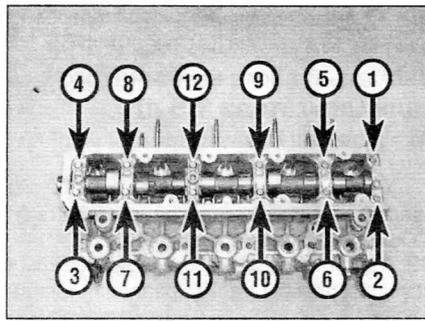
Последовательность отпускания болтов крепления корпуса подшипников распределительного вала (двигатели 2.0 л)
